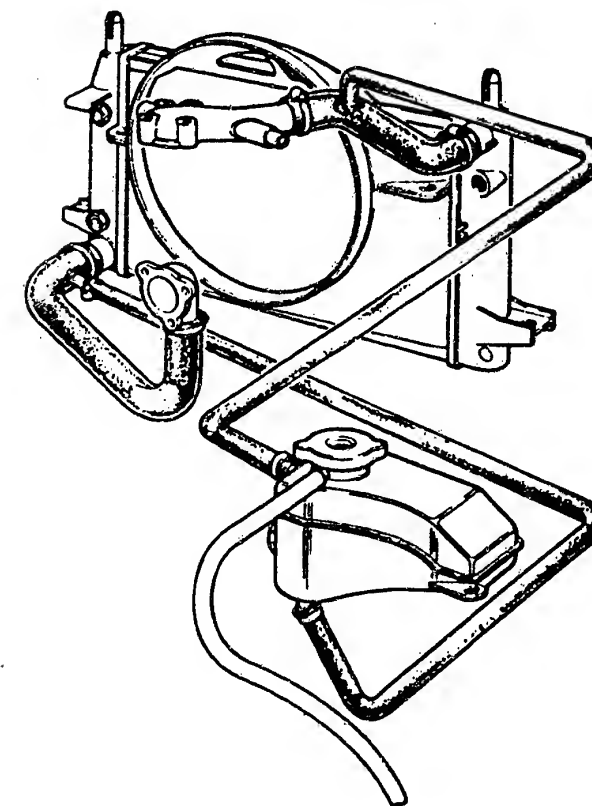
Kühlsystem des V6-Motors ohne die Heizschläuche.
